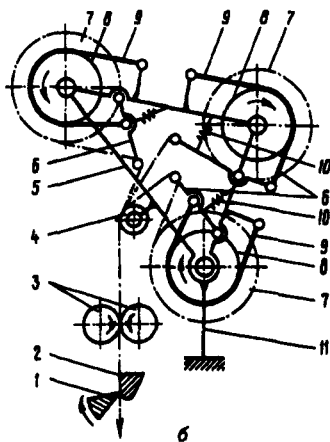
Питатель упаковочного материала машины ЗКЦА
